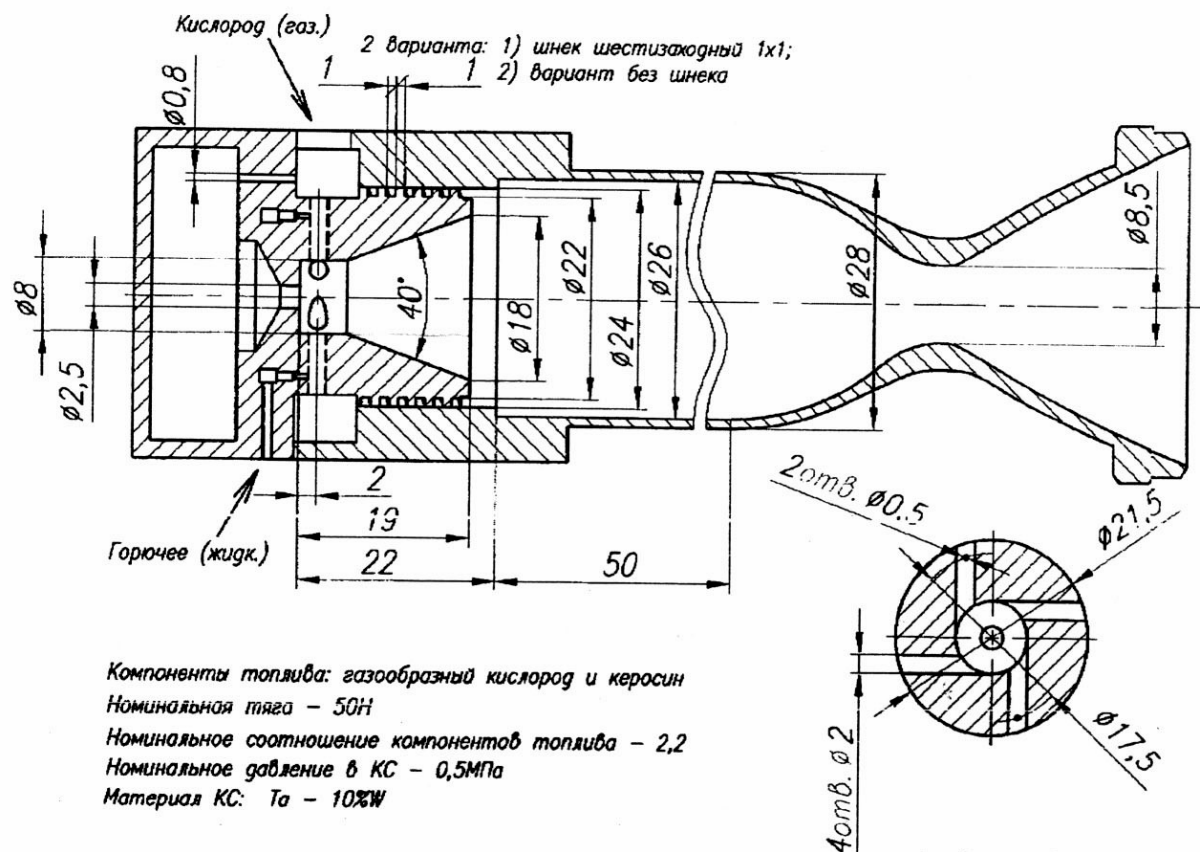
Конструкция рассчитываемой камеры двигателя
